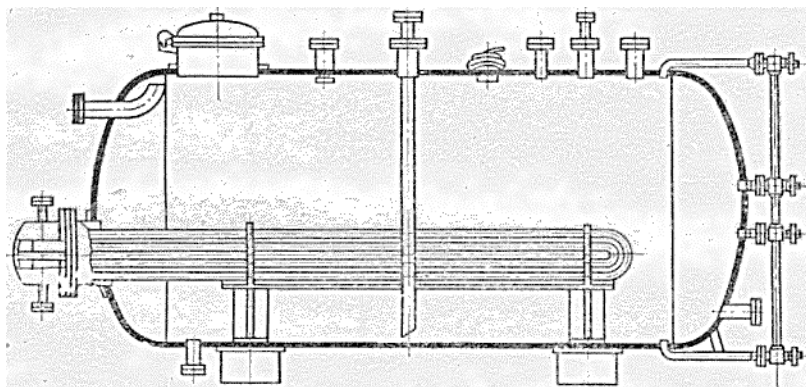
Горизонтальный цилиндрический резервуар с U-образным греющим элементом
